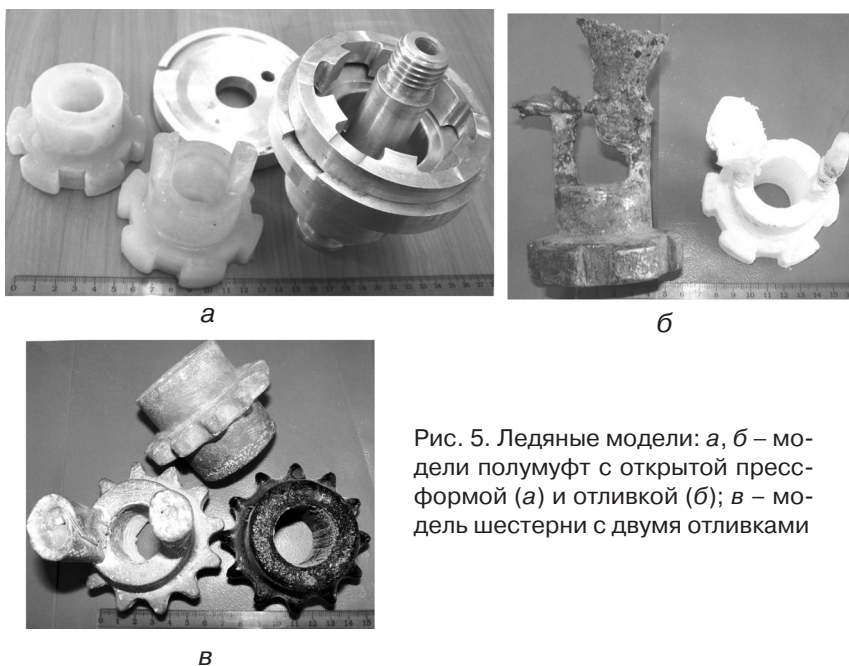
Ледяные модели: а, б – модели полумуфт с открытой пресс-формой (а) и отливкой (б); в – модель шестерни с двумя отливками
